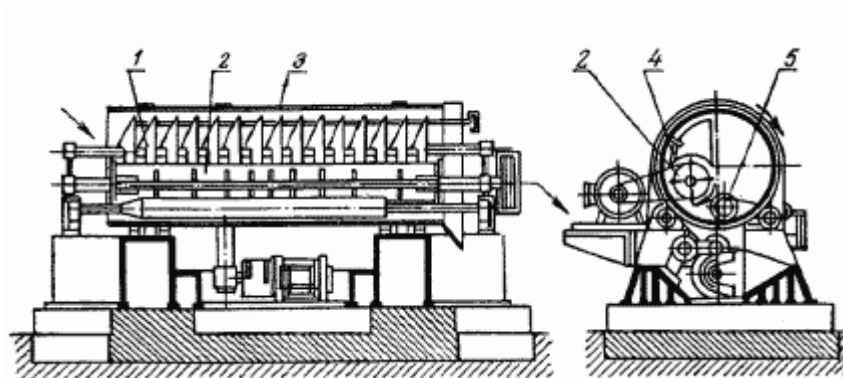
Установка для приготовления формовочных и стержневых смесей с аэратором
